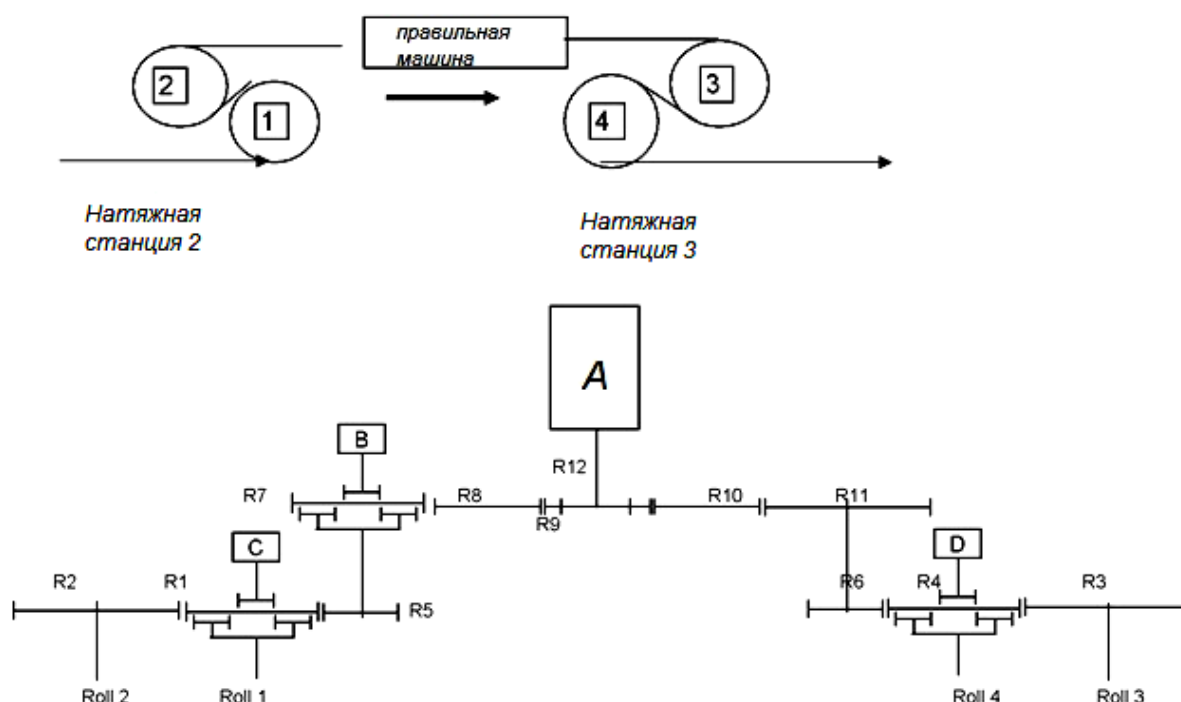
Схема расположения зубчатых колес редукторов ИРМ:
